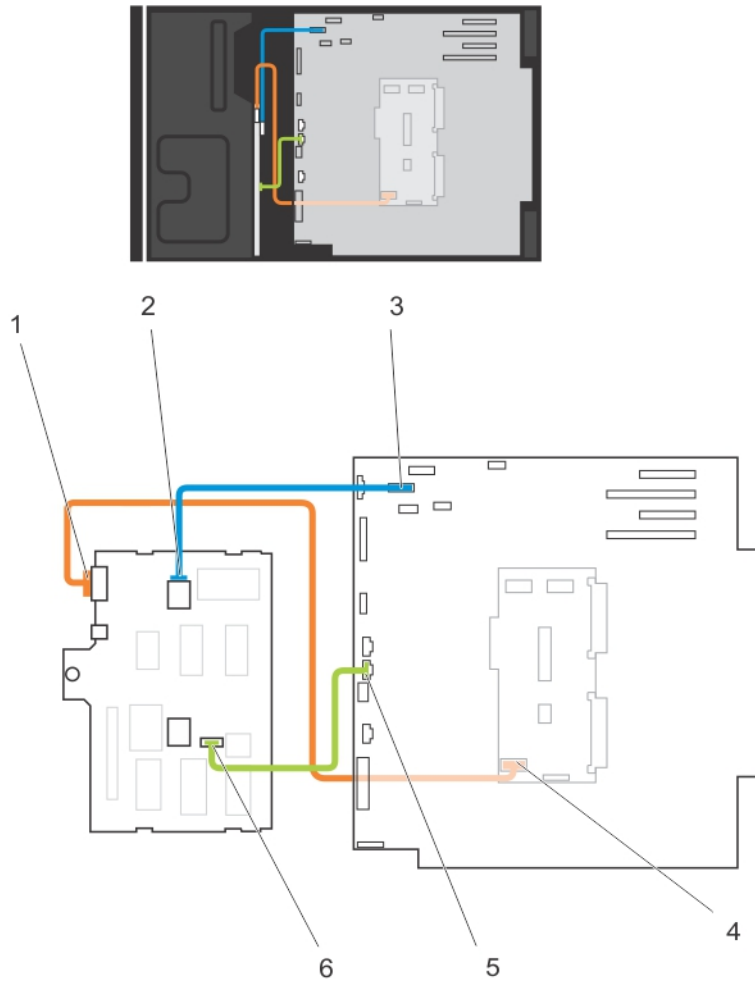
Câblage - Fond de panier SAS/SATA de 3,5 pouces (x8)
